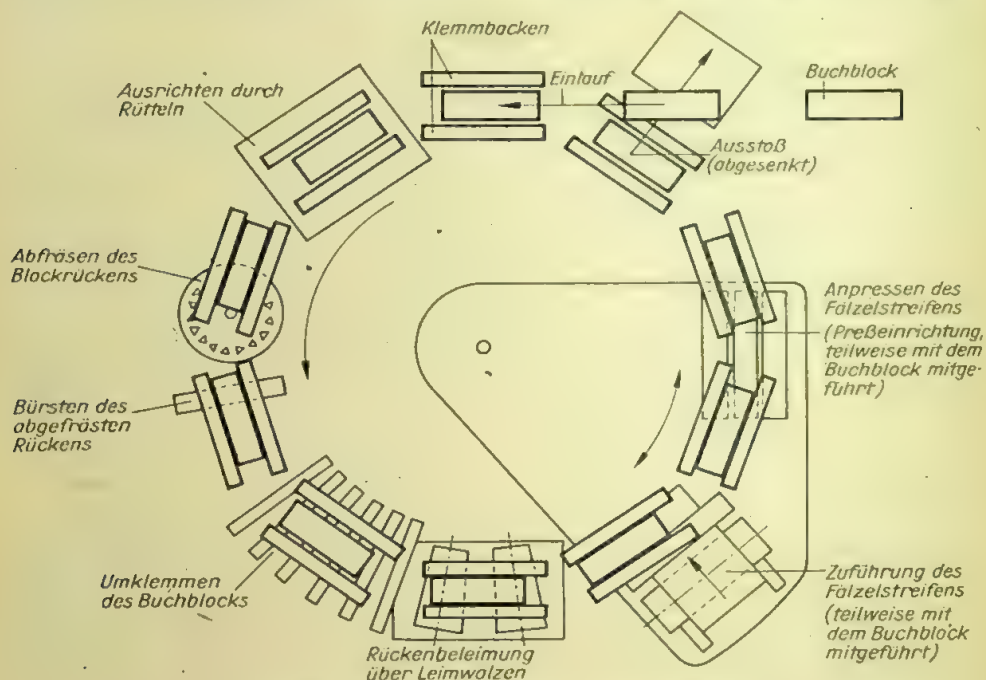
Schema der Bearbeitungsstationen einer Klebebindemaschine
